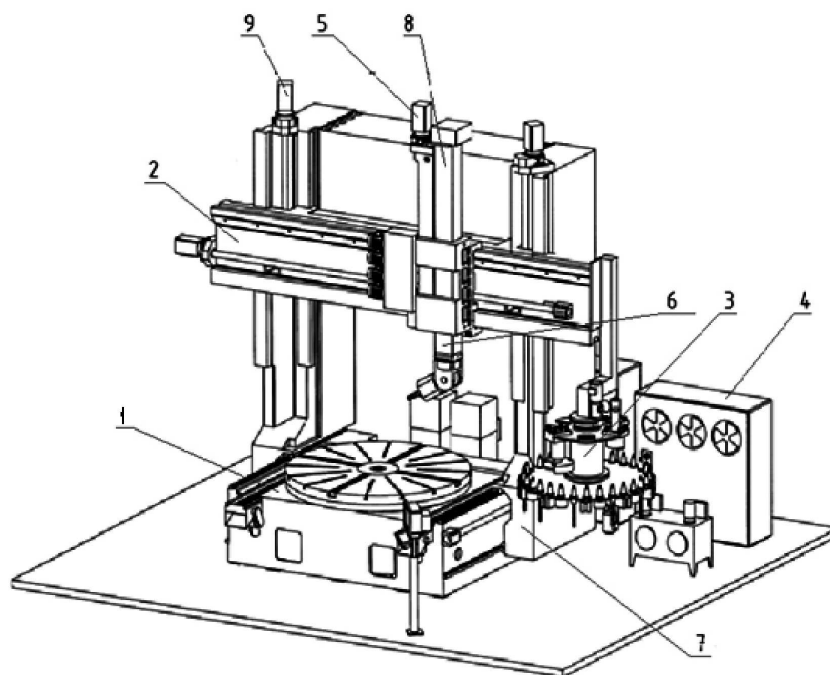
Многоцелевой станочный комплекс VM 32:
